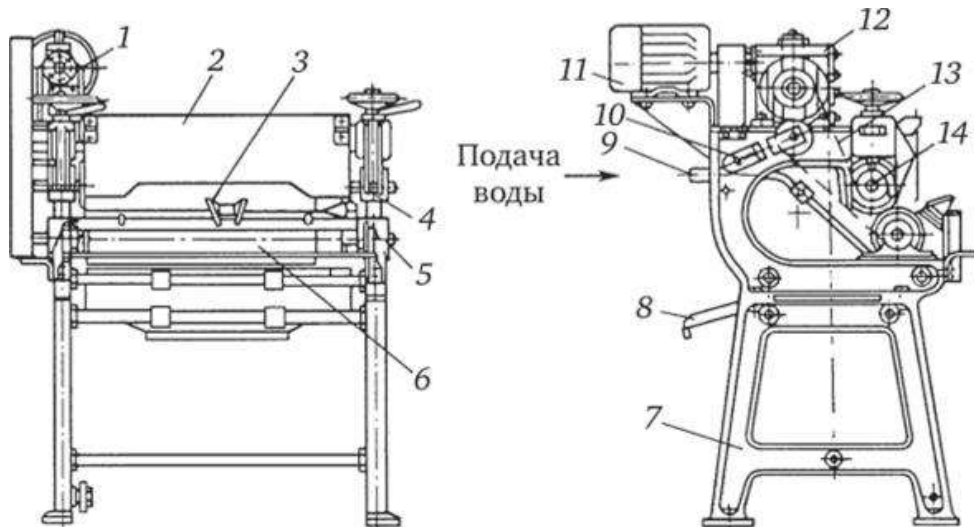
Відтискні вальці Г2-ФОД: 1 – кожух; 2 – запобіжний щиток, 3 – завантажувальний пристрій, 4 – маховик; 5 – рухомий підшипник; 6, 14 – вальці; 7 – станина, 8 – відвідний лоток; 9 – зрошувач; 10 – натяжний пристрій; 11 – електродвигун; 12 – редуктор, 13 – ланцюгова передача
